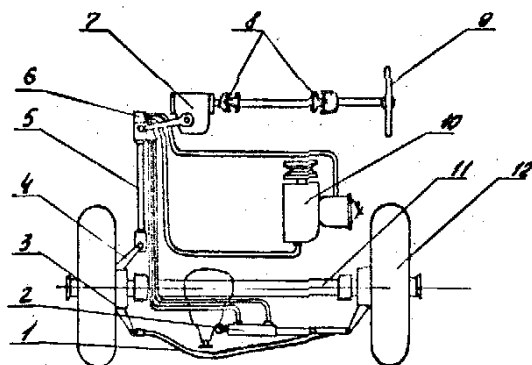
Схема рульового керування автомобіля: 1 – поперечна тяга; 2 – силовий циліндр гідропідсилювача; 3 – нижній важіль поворотної цапфи; 4 – верхній важіль поворотної цапфи; 5 – поздовжня тяга; 6 – клапан керування; 7 – рульовий механізм; 8 – шарніри рульового вала; 9 – рульове колесо; 10 – насос гідропідсилювача; 11 – передній міст; 12 – керовані колеса
